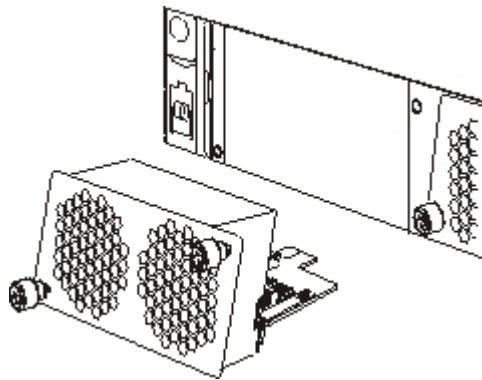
Removendo um módulo de ventilador em um dispositivo Tipo 7198
